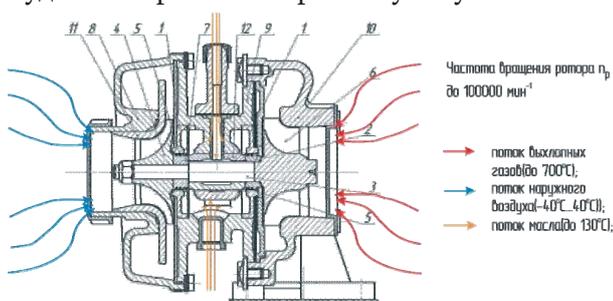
Общий вид турбокомпрессора: 1 – крышка уплотнения; 2 – втулка вала ротора; 3 – вал ротора; 4 – колесо компрессора; 5 – уплотнительные кольца; 6 – колесо турбины; 7 – маслоотражатель; 8 – корпус компрессора; 9 – корпус средний; 10 – корпус турбины; 11 – вставка компрессора; 12 – подшипник
